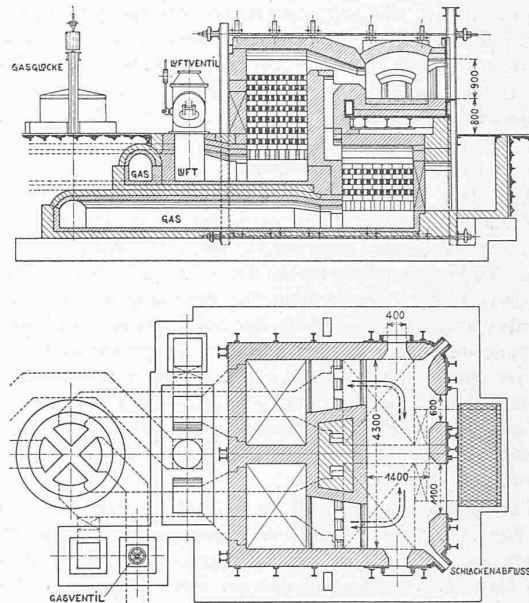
Schmiedeofen zum Wärmen von Maschinenteilen, mit Gasfeuerung und Regenerator. — Masstab 1:150.
